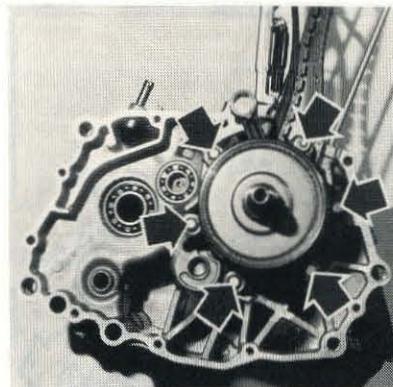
Les six fixations du palier central du vilebrequin (Photo RMT)
